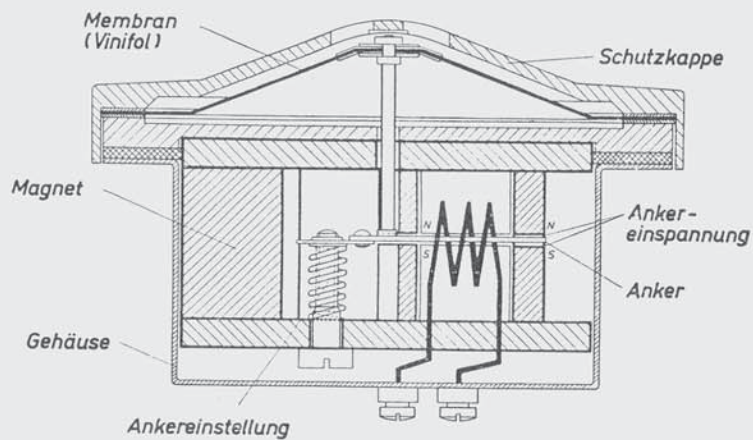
System für Festungsfernörer 39, magnetisch, Schnittzeichnung
